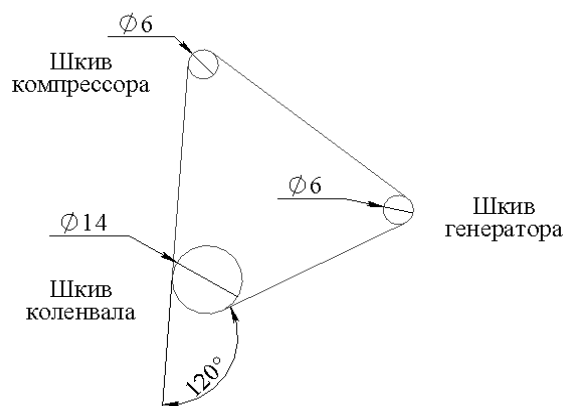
Расположение ремня и шкивов для привода генератора и компрессора
